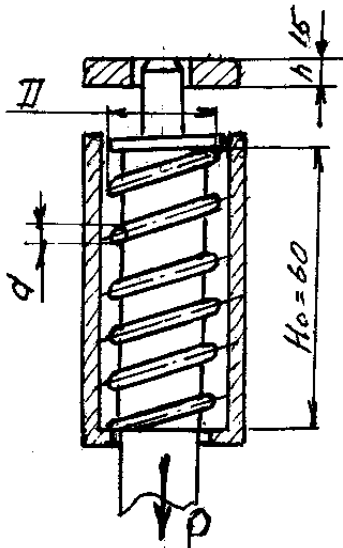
Розрахункова схема пружини фіксатора
